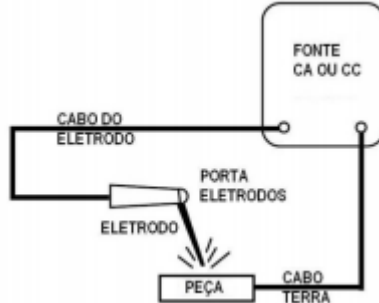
Região do arco na soldagem com eletrodos revestidos.
